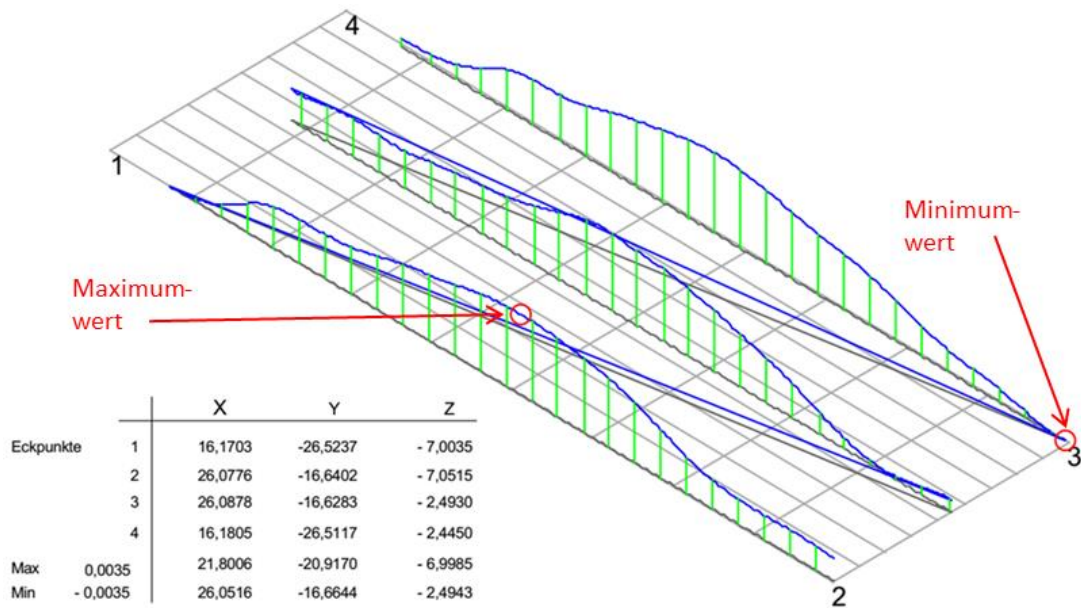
Messprotokoll über die Ebenheit einer geschliffenen Fläche eines im Gleichlauf bearbeiteten Achtkantprofils
